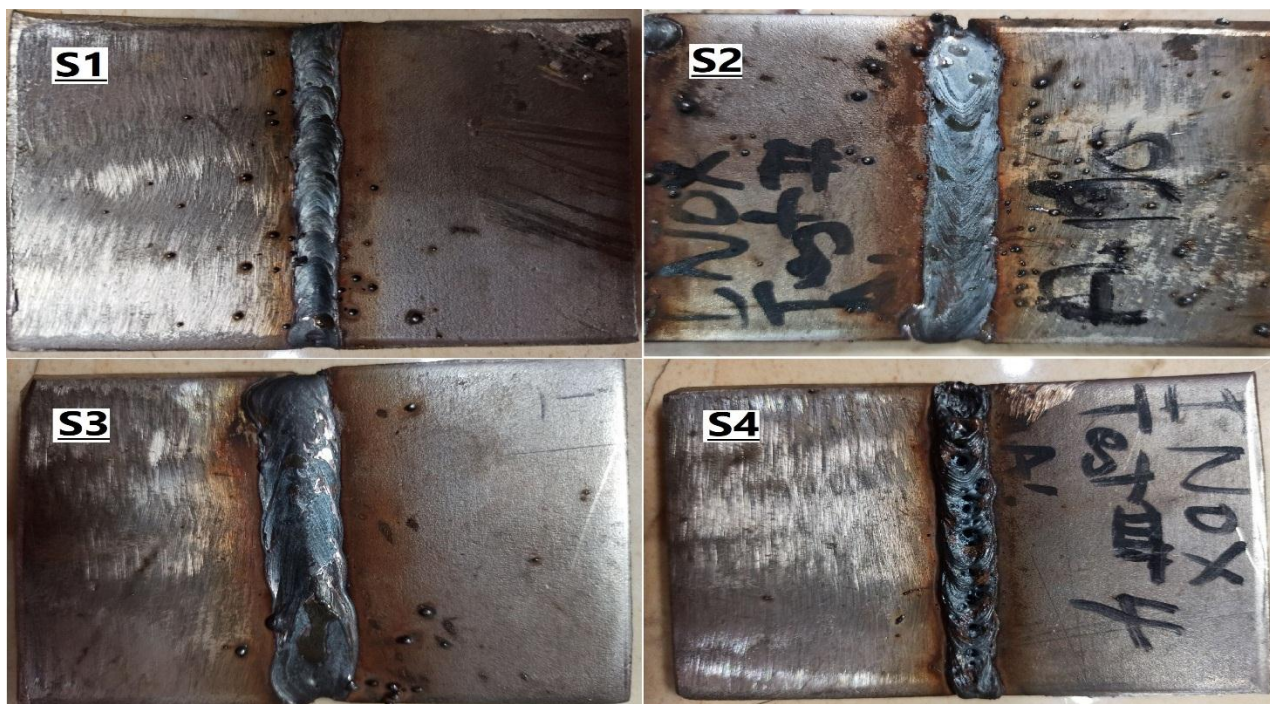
Éprouvettes N°3 après soudage.
